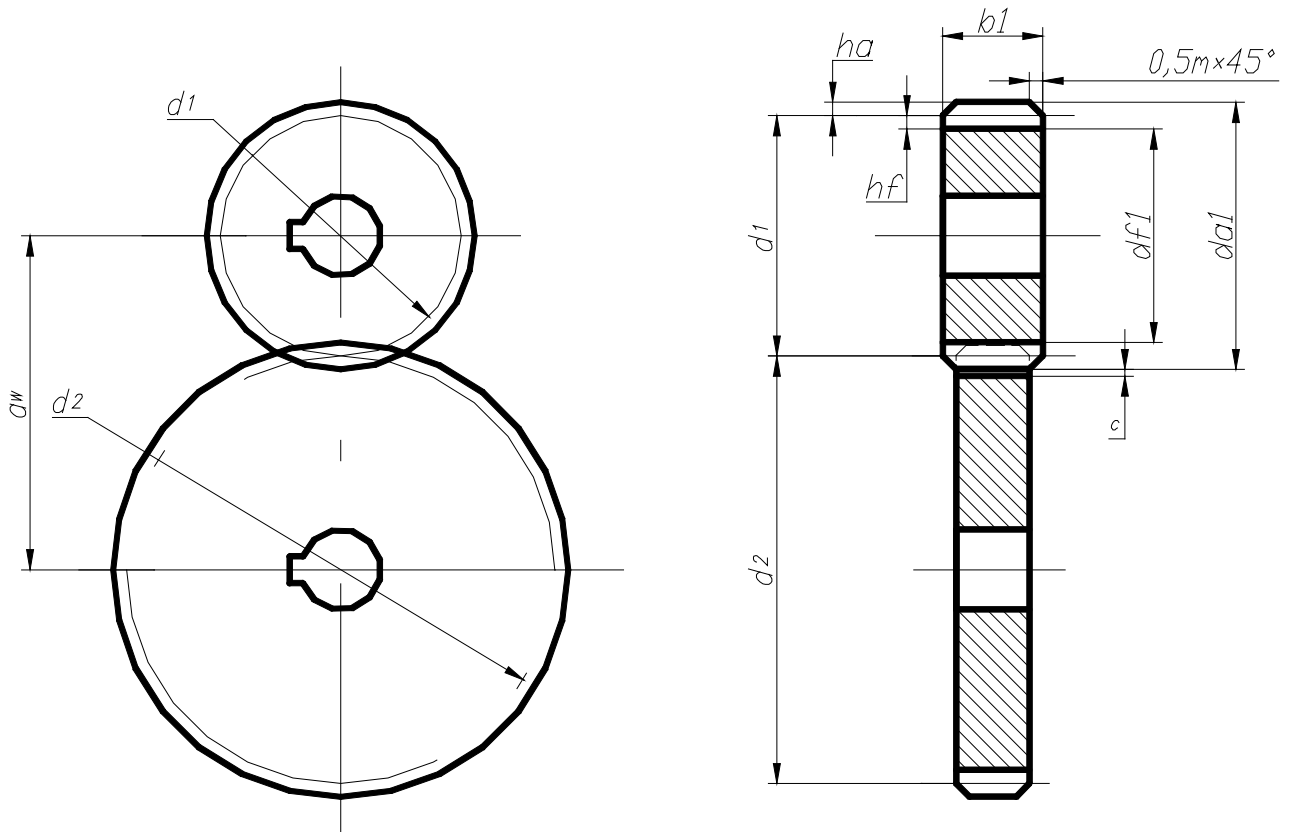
Схема зубчастої передачі приводу пресуючого шнека преса
